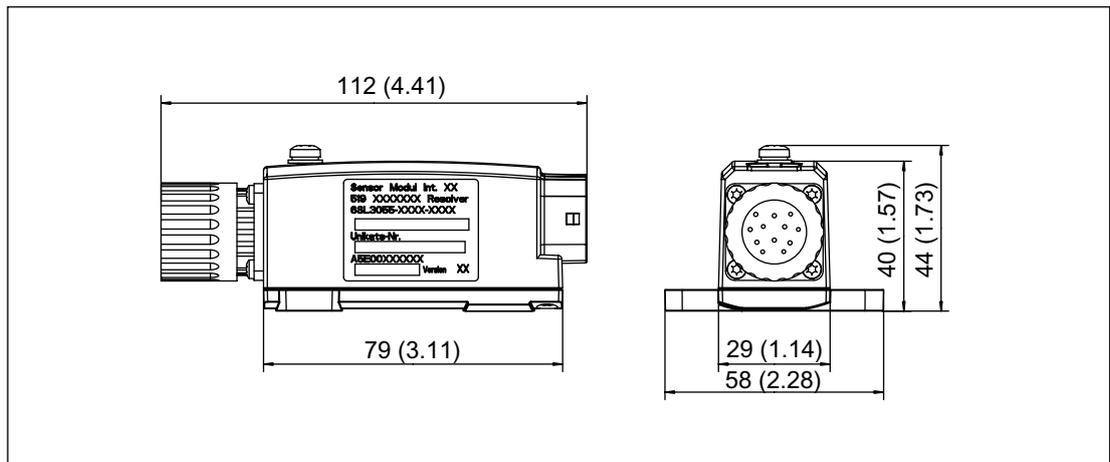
Maßbild SME20, Bestellnummer 6SL3055-0AA00-5EA0
